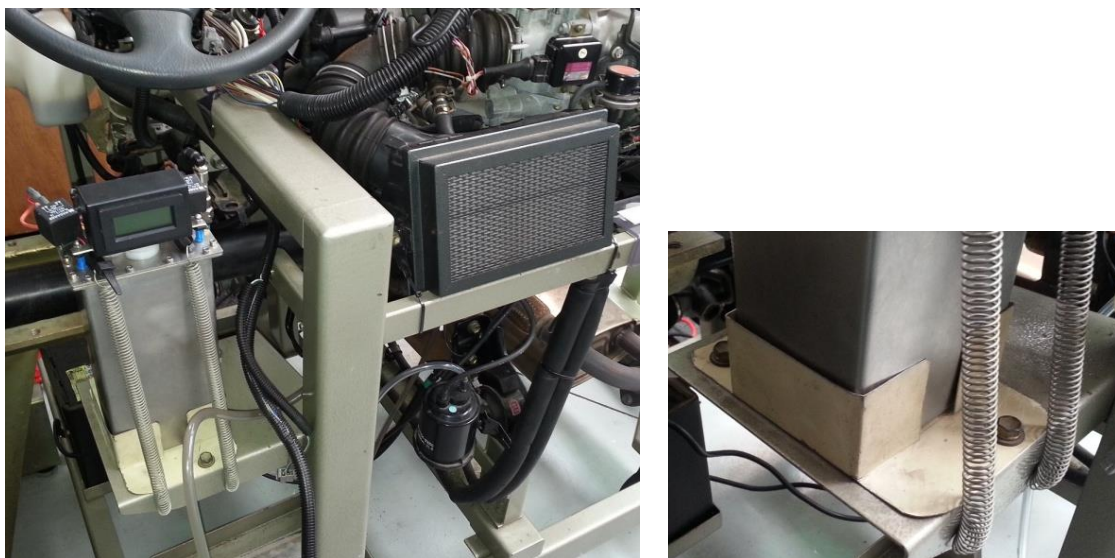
À esquerda o aspeto do conjunto montado e à direita o suporte feito em chapa
